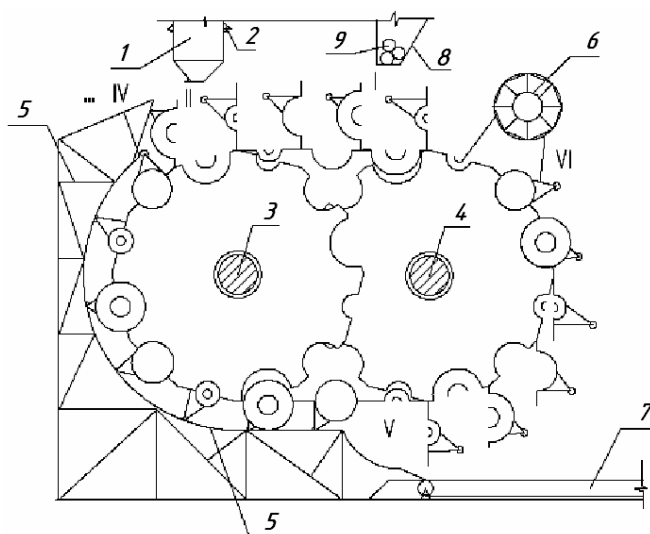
Схема установки для изготовления трубопроводов с пенополимербетонной изоляцией барабанного действия: 1 — смеситель; 2 — направляющие; 3 — ведущий вал; 4 — ведомый вал; 5 — обжимная рама с направляющими полозьями; 6 — откидыватель; 7 — транспортер; 8 — питатель трубами; 9 — трубы. I — позиция укладки труб в формы; II — позиция заливки смеси в форму; III — позиция неполного закрытия формы; IV — позиция полного закрытия формы; V — позиция извлечения готовых изделий; VI — позиция открытия формы
